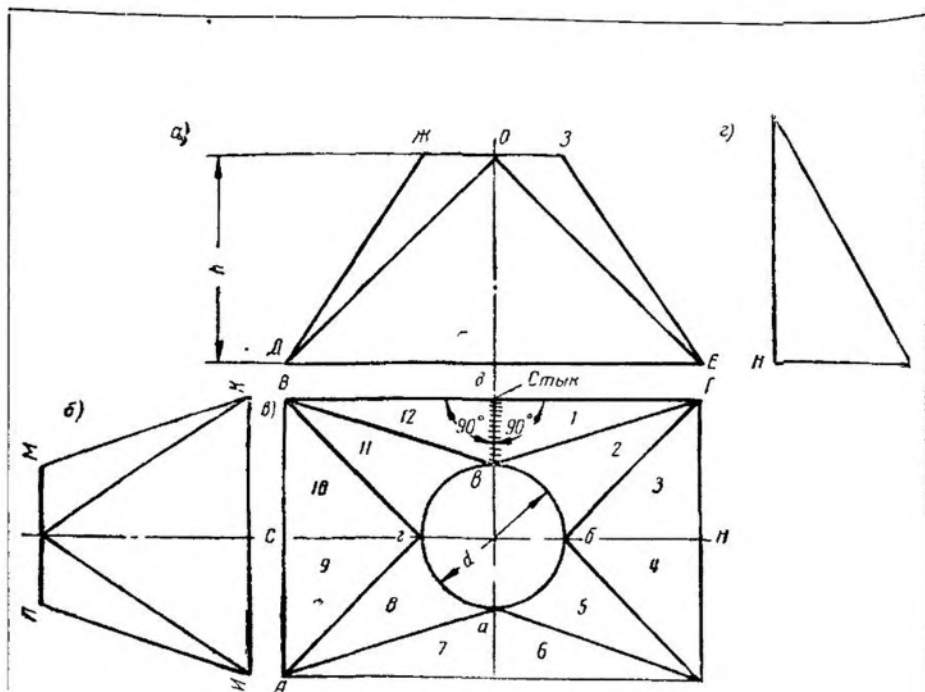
Развертка перехода с прямоугольного на круглое сечение
